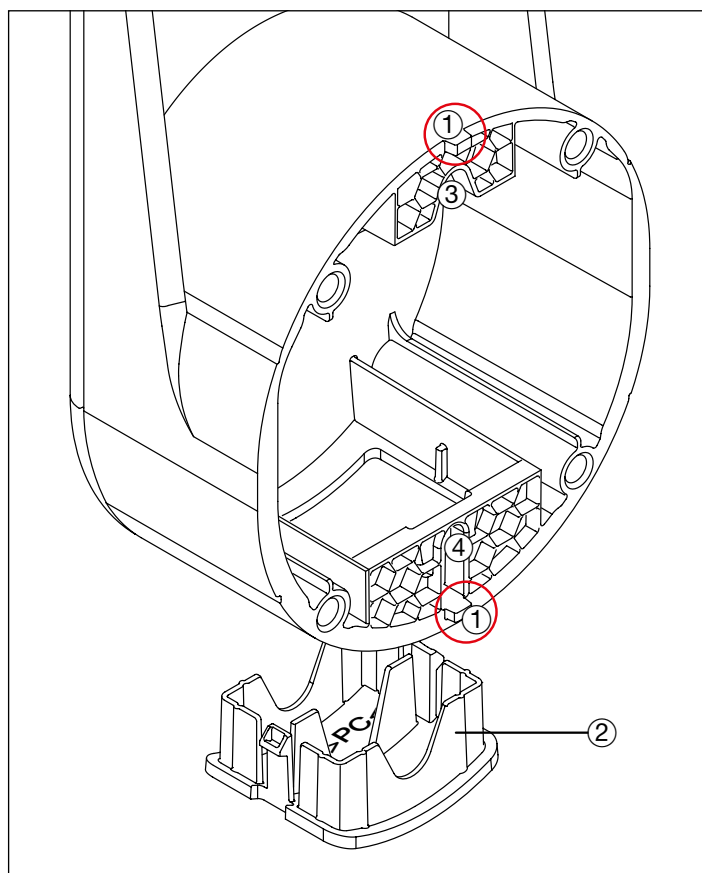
Montaje del soporte para cables en la pared (vista desde atrás)
